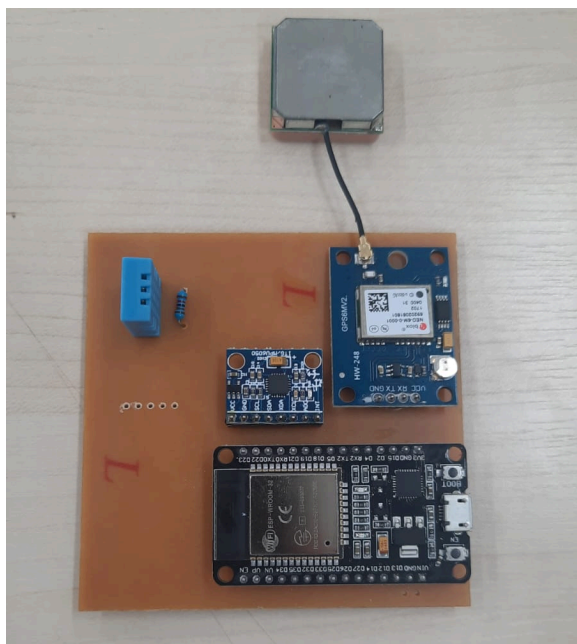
Componentes eletrônicos montados e soldados na placa.
